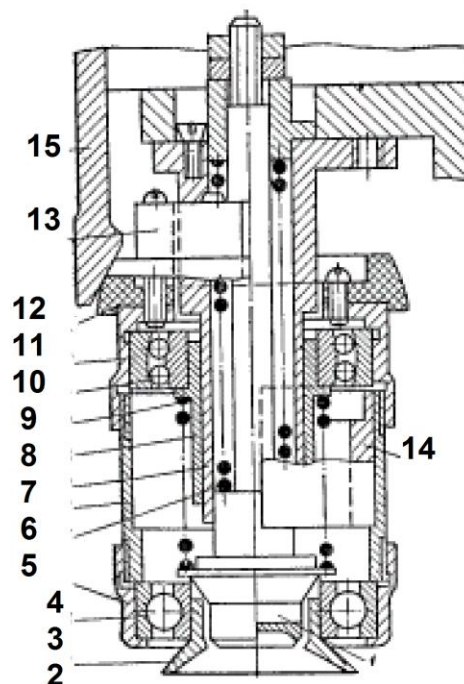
Обкатний безроликаний закупорювальний механізм
